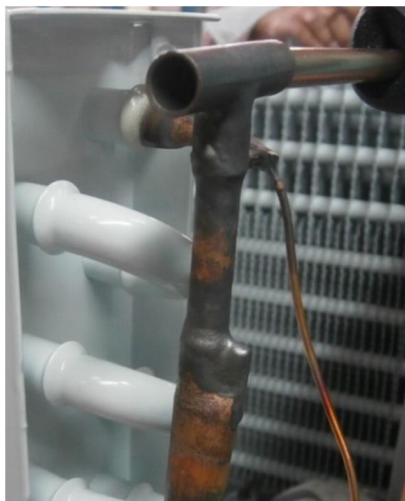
Operação de soldadura da saída do evaporador
